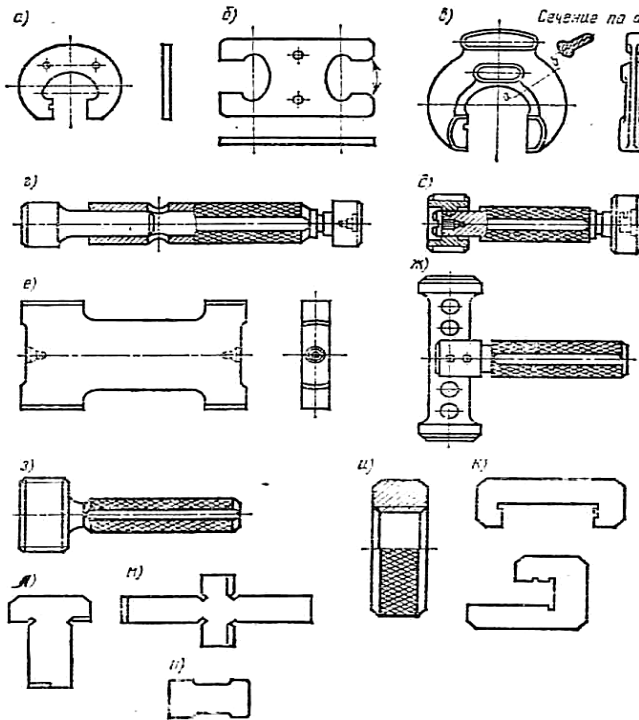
Безшкальний контрольно-вимірювальний інструмент
